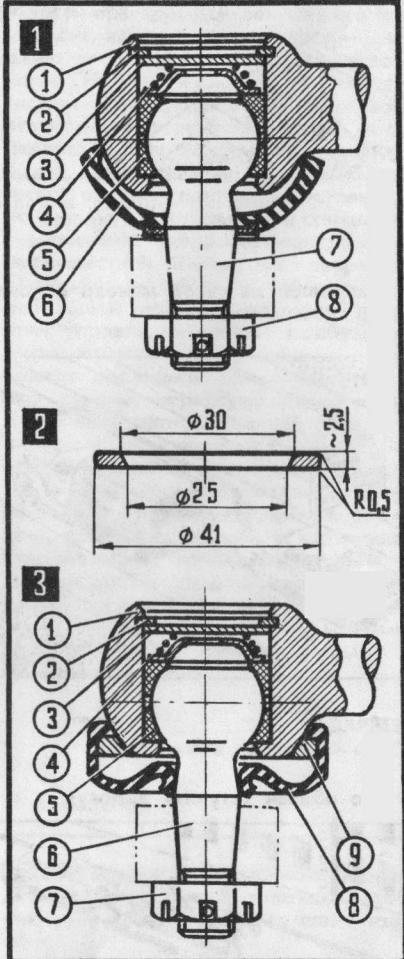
Заводская конструкция: 1 — рулевая тяга; 2 — стопорное кольцо; 3 — заглушка; 4 — пружина; 5 — вкладыш; 6 — защитный чехол; 7 — палец; 8 — гайка.
